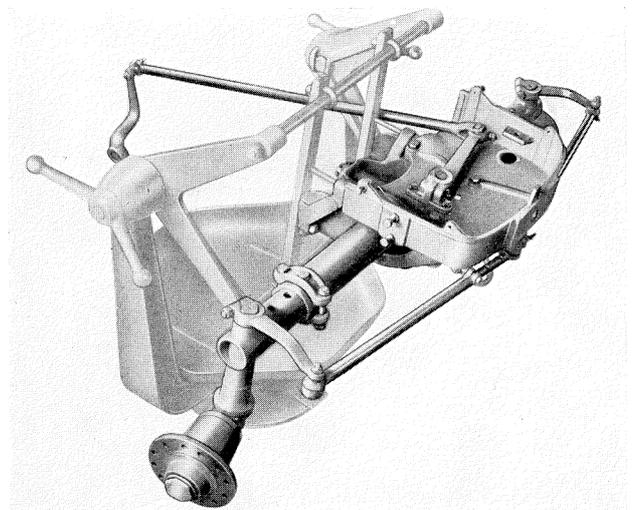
Essieu avant monté pour la révision sur le chevalet pivotant.
